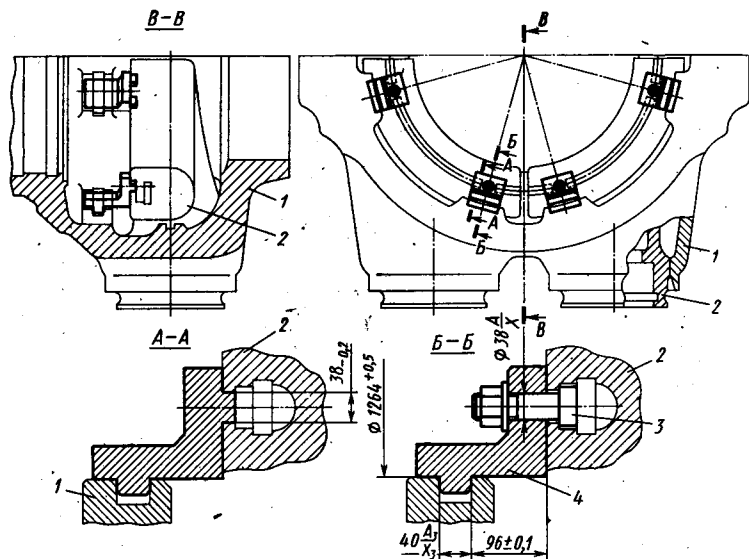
Приспособление для сборки под сварку внутреннего цилиндра турбины Р-100/130 с сопловыми коробками:
